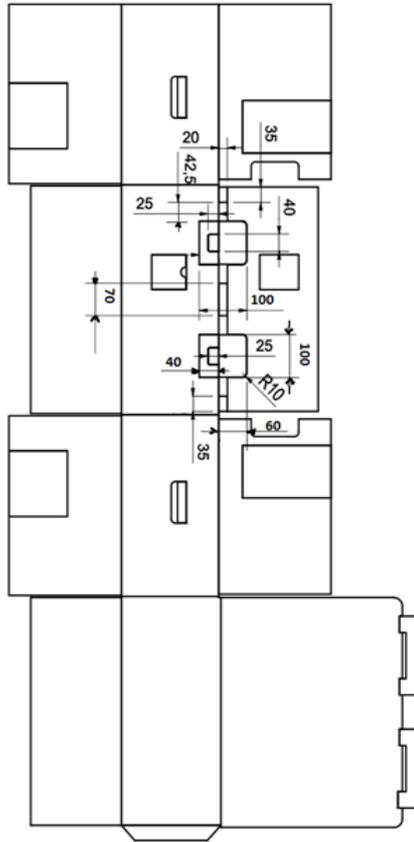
Caixa planificada somente com as medidas do sistema de fechamento (lingueta, puxador) – dimensionamento para corte
